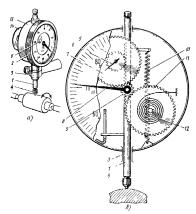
Индикатор часового типа: a — общий вид,  $\delta$  — схема зубчатой передачи
